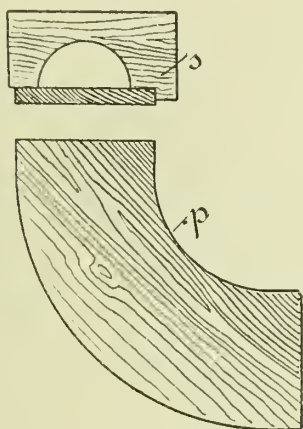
Ziehplatte mit Schablone für gebogene Kerne.
